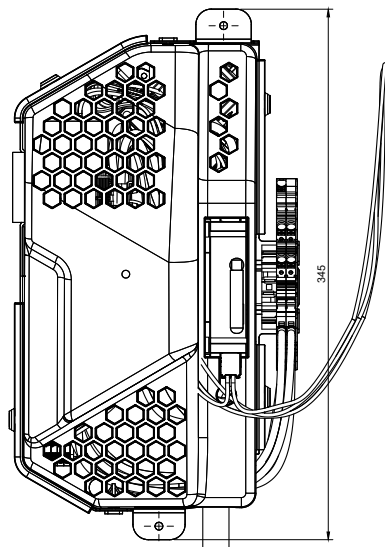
Seitenansicht Wallbox (rechts); ohne Ladestecker
